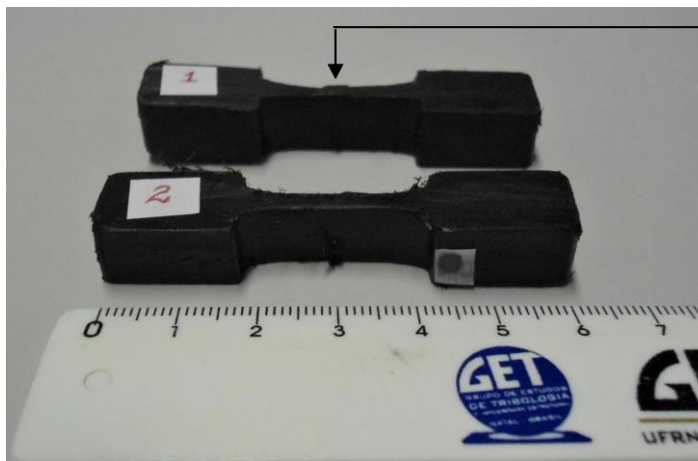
Corpos de prova em PEAD (1) Com cordão de solda, (2) Sem cordão de solda.
